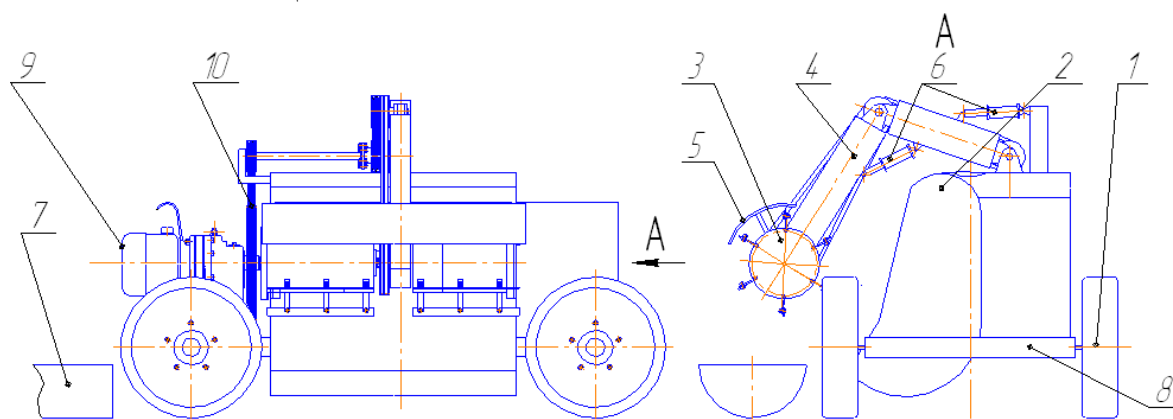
Устройство для очистки кормушек 1 – Ходовая часть; 2 – бункер; 3 – очищающий барабан; 4 – стрела; 5 – кожух; 6 – силовой гидроцилиндр; 7 – кормушка; 8 – рама; 9 – мотор-редуктор; 10 – передача ременная;
